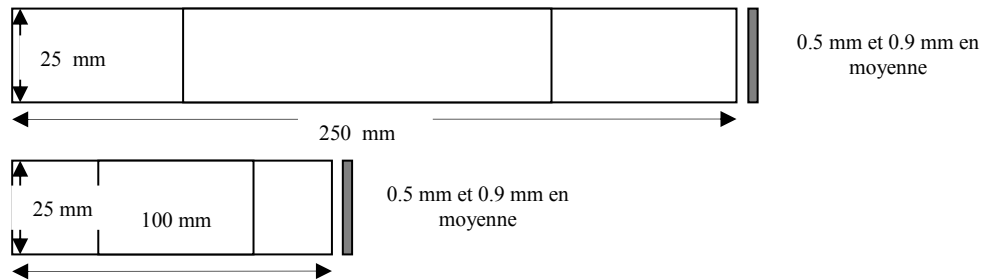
Dimensions des éprouvettes. en haut, éprouvette normée; en bas, non normée
